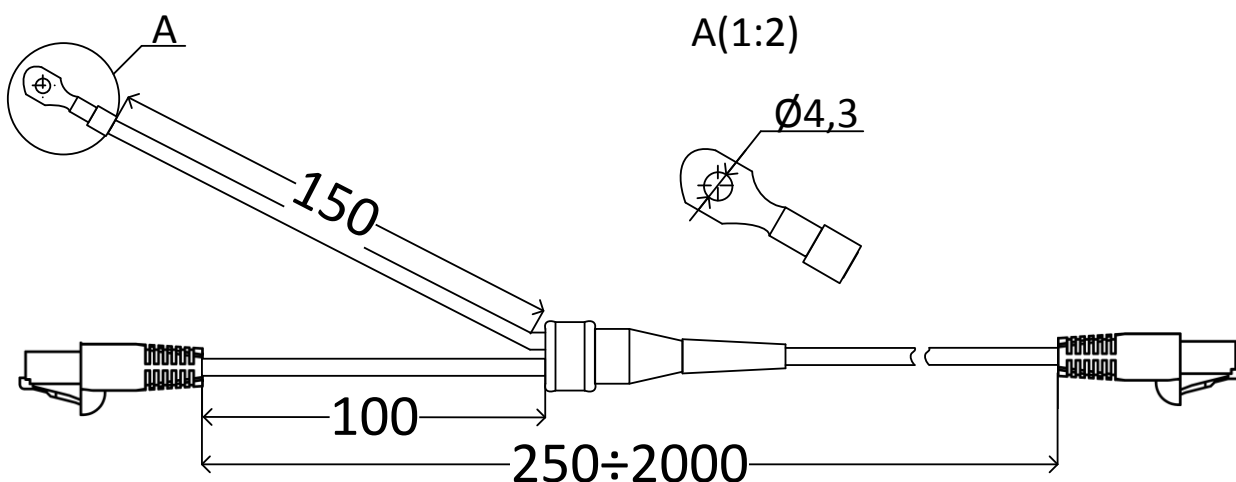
Габаритные размеры устройства Commeng Cat5P-PC
